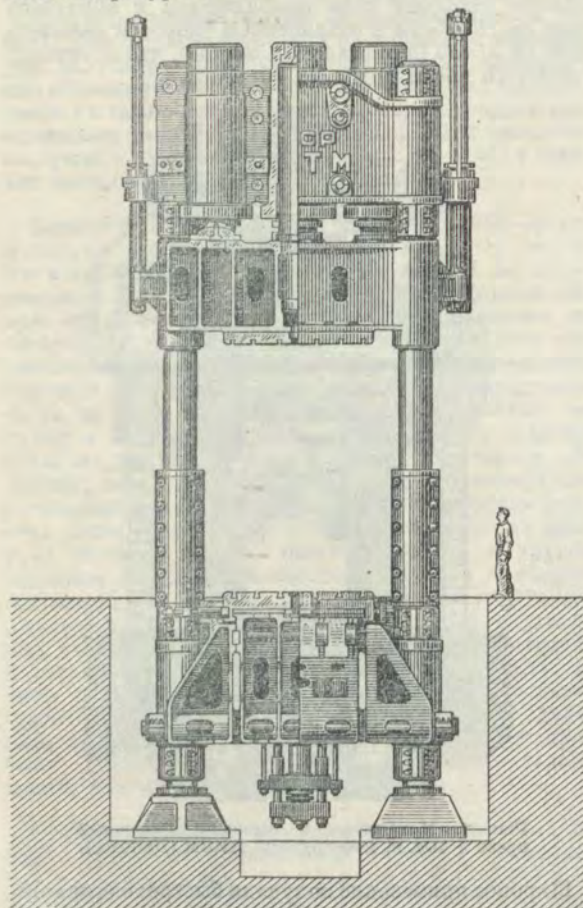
Чистогидравлический ковочный пресс 6 тыс. т конструкции УЗТМ.
